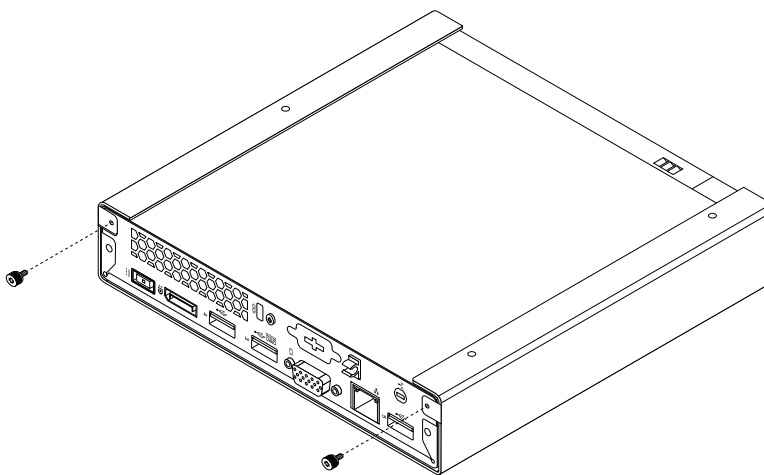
Installazione delle viti che fissano la staffa di montaggio VESA
